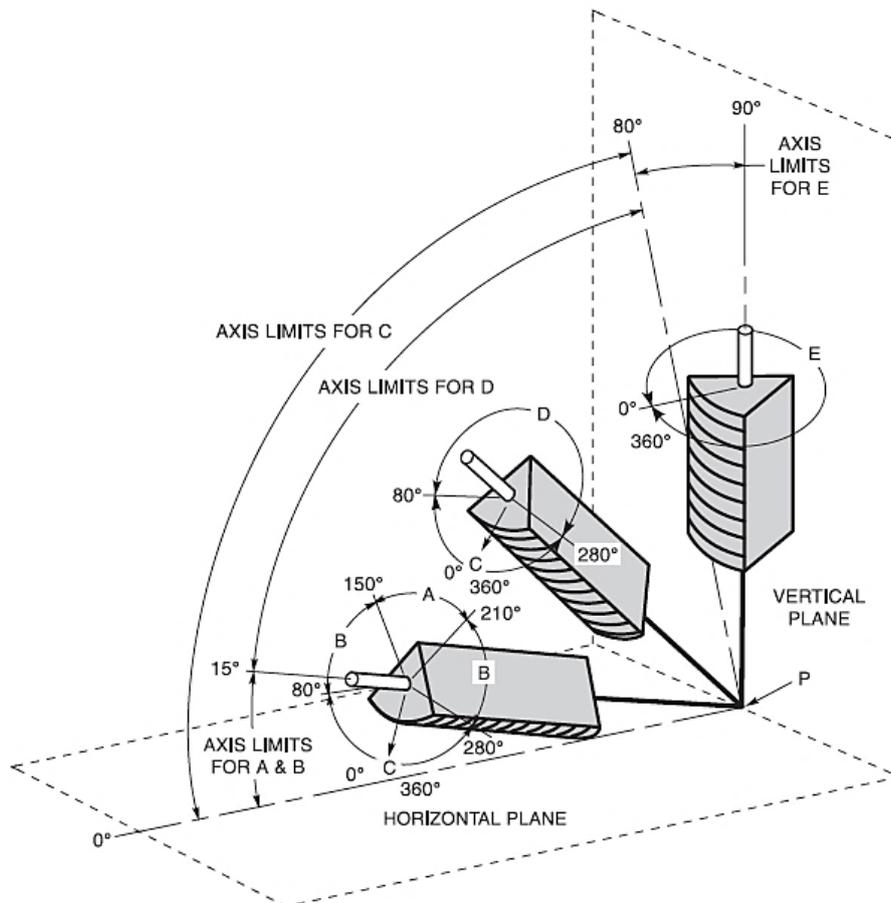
Esquema de posiciones de soldadura a tope.
